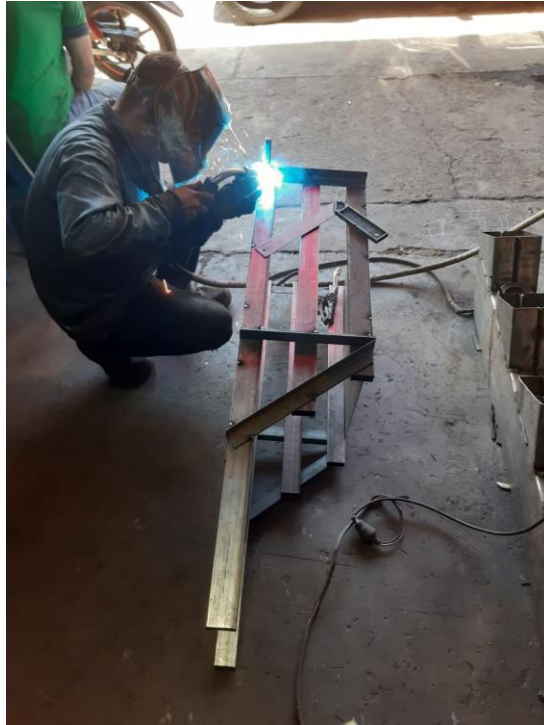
Armado inicial de la estructura principal (vista posterior)
